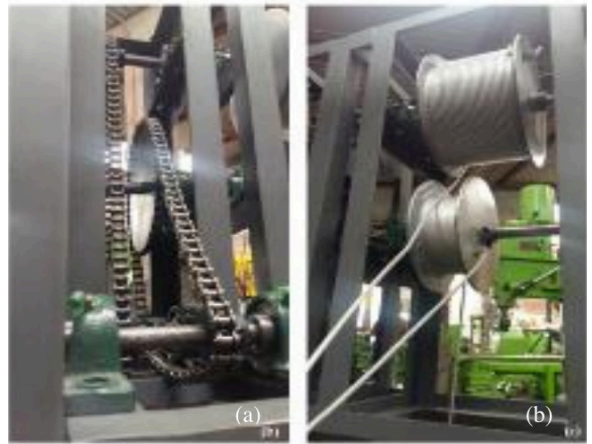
Montaje de elementos mecánicos. (a) Montaje de catarinas y cadenas y (b) Montaje de carretes con el mecanismo de transmisión.
